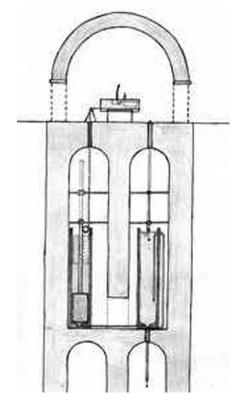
Sección transversal del mecanismo de giro automático de la luminaria
